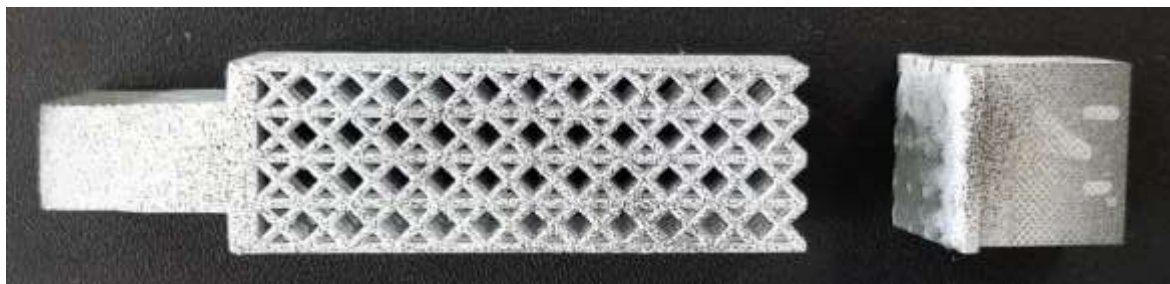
Разрушенный образец с ЭЯП f2ccz
